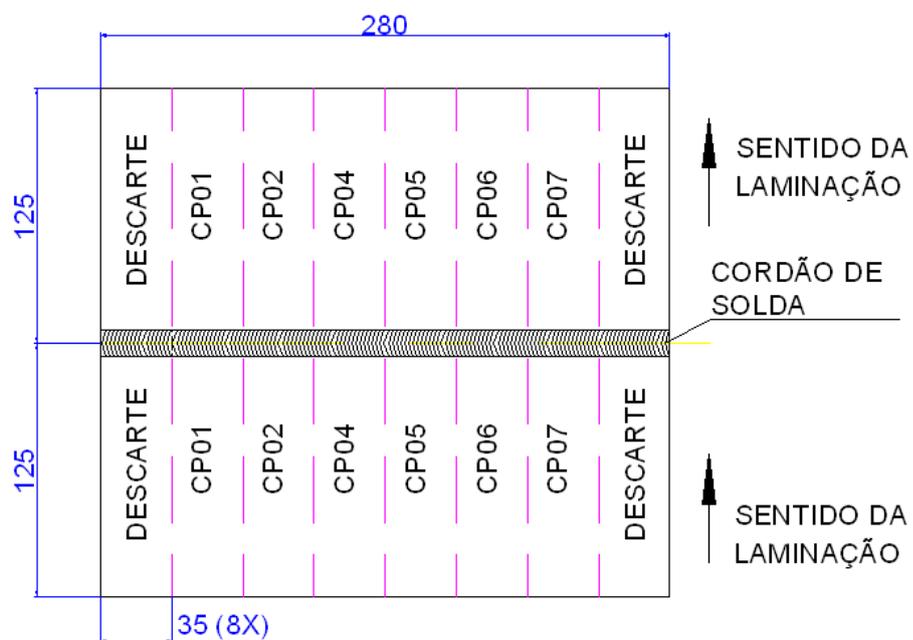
Disposição dos corpos de prova na chapa soldada (ASME IX)
